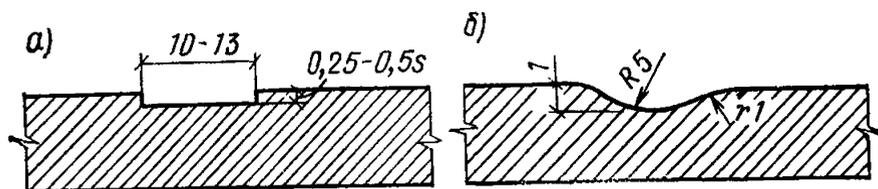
Ориентировочные размеры и формы канавок в съемных подкладках для сварки стыковых соединений алюминиевых элементов толщиной до 3 мм
